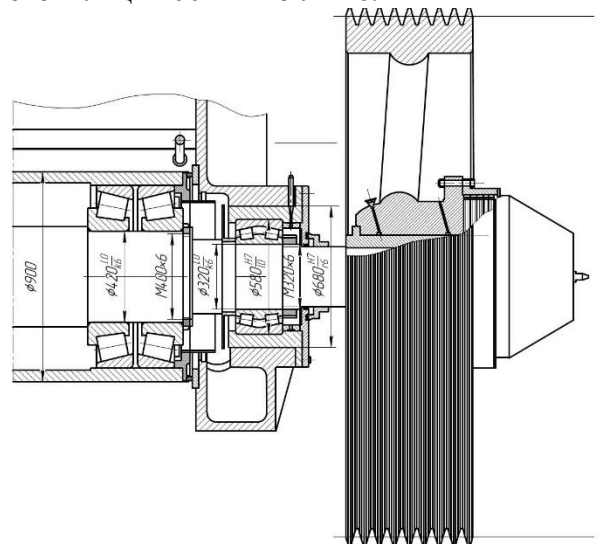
Переріз підшипникового вузла ексцентрикового вала шоківі дробарки.
